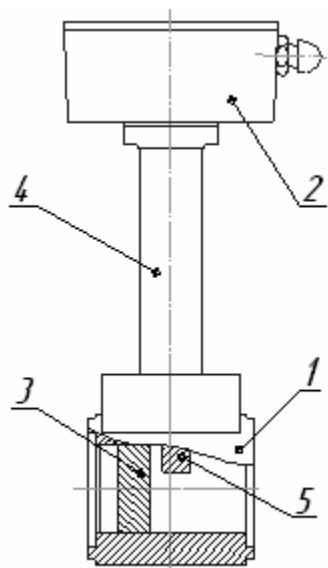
Устройство преобразователя расхода , 1 - корпус; 2 – электронный блок (корпус прямоугольной формы); 3 – тело обтекания; 4 – стойка; 5-чувствительный элемент;
